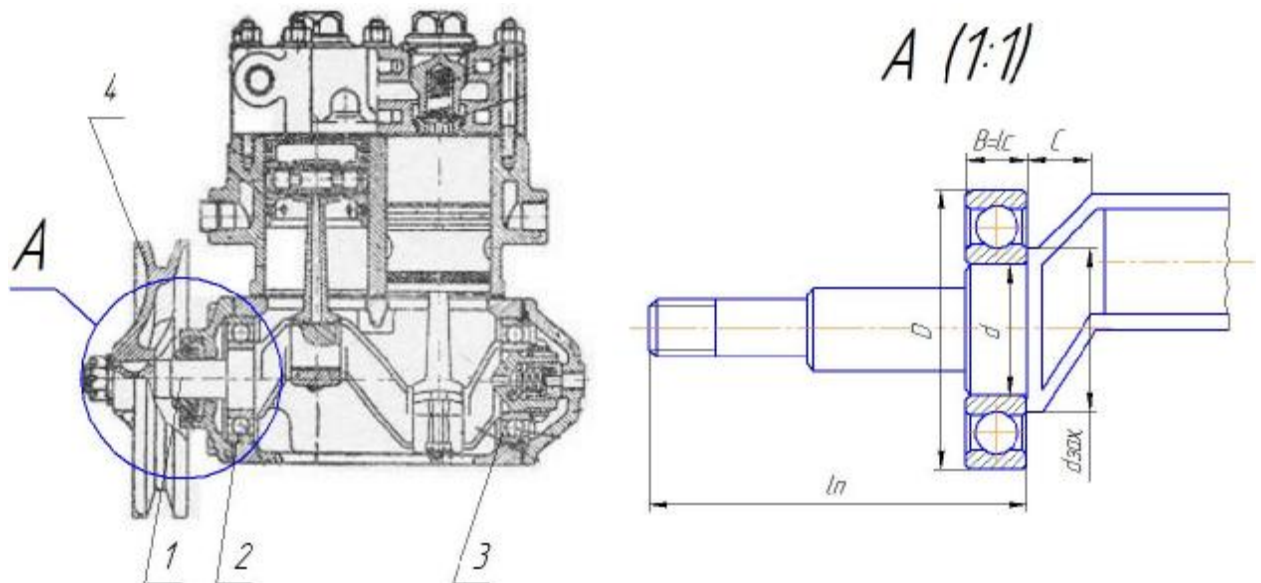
Схема встановлення кулькового підшипника на колінчастому валу компресора автомобіля КамАЗ-65115: 1 – колінчастий вал; 2 – підшипник передньої опори вала; 3 – підшипник задньої опори вала; 4 – шків.
